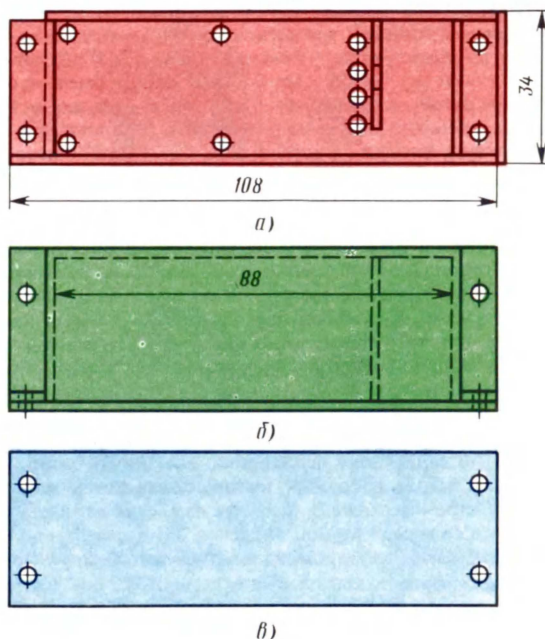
Конструкция корпуса высоковольтной части ГСН: а — вид сверху; б — вид сбоку; в — крышка
